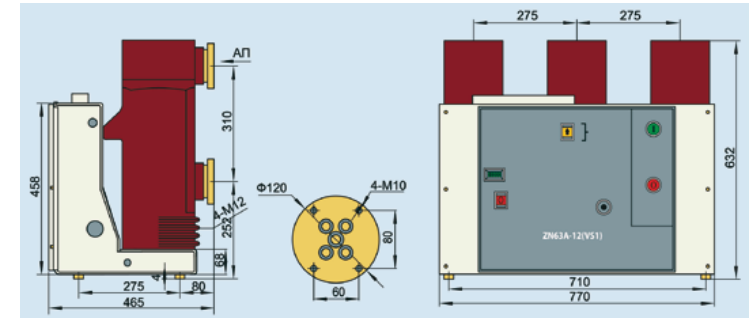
Внешний вид и монтажные размеры выключателя ZN63A-12/T - 40
